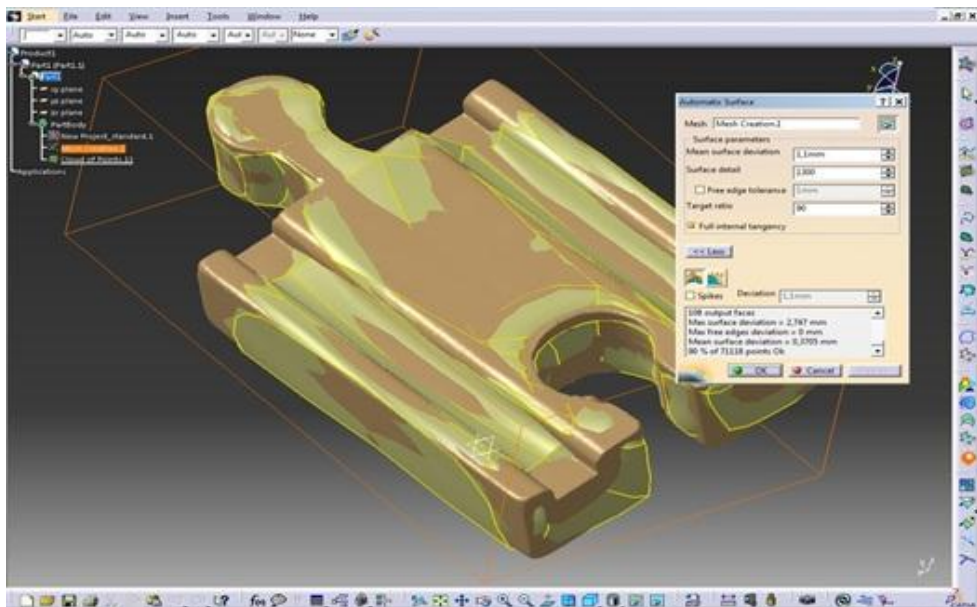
Shape – modul *Quick Surface Reconstruction
